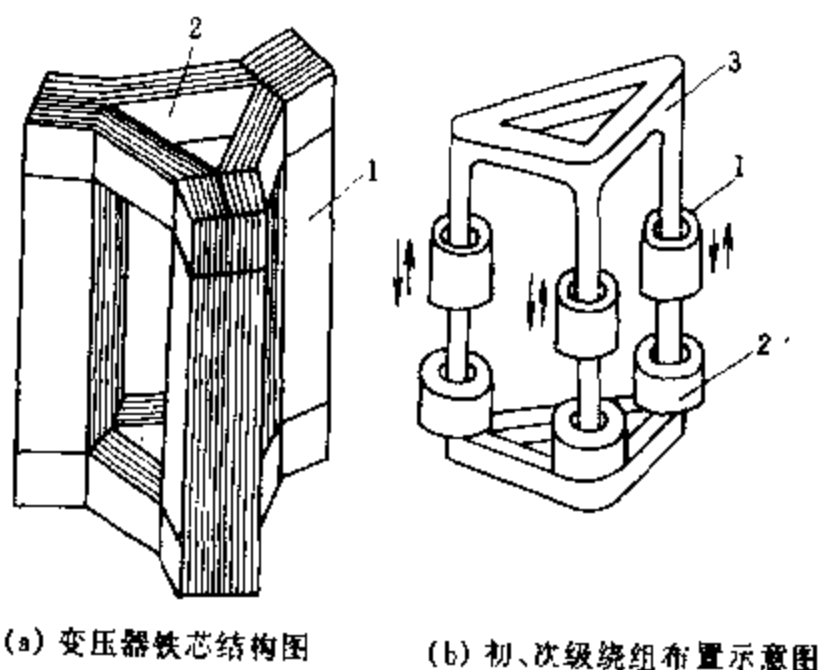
三相动圈式硅整流焊机变压器结构示意图
